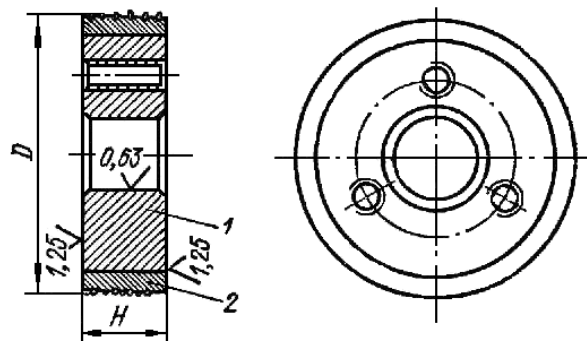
Эскиз ролика с алмазосносным слоем для правки абразивных инструментов: 1 – корпус; 2 – алмазосносный слой
